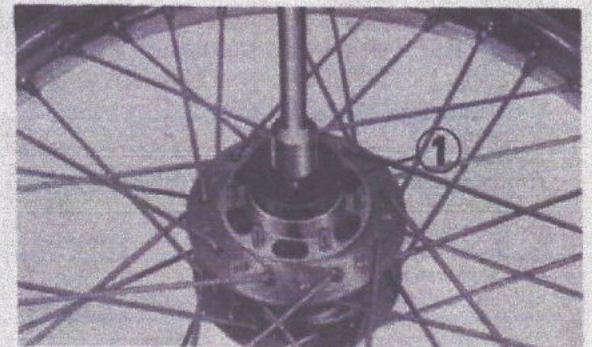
(1) Clé de démontage de flasque de roulement à billes
